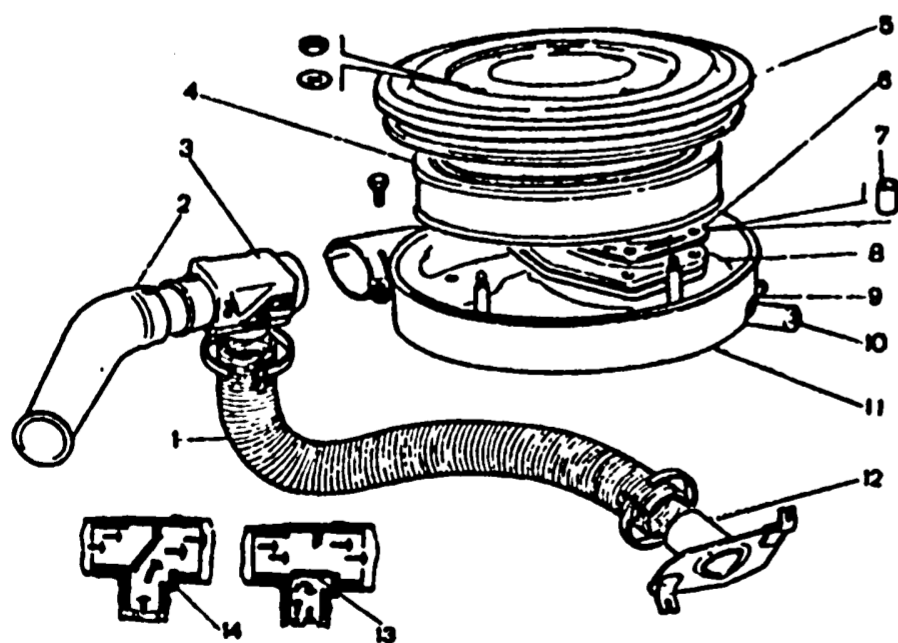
Детали воздушного фильтра: 1 - шланг воздухозаборника теплого воздуха; 2 - заборник холодного воздуха; 3 - терморегулятор; 4 - фильтрующий элемент; 5 - крышка; 6 - пластина крепления фильтра; 7 - дистанционная втулка; 8 - прокладка; 9 - патрубок для отвода картерных газов к золотниковому устройству карбюратора; 10 - вытяжной коллектор картерных газов; 11 - корпус воздушного фильтра; 12 - воздухозаборник теплого воздуха; 13 - заслонка терморегулятора; 14 - корпус терморегулятора
